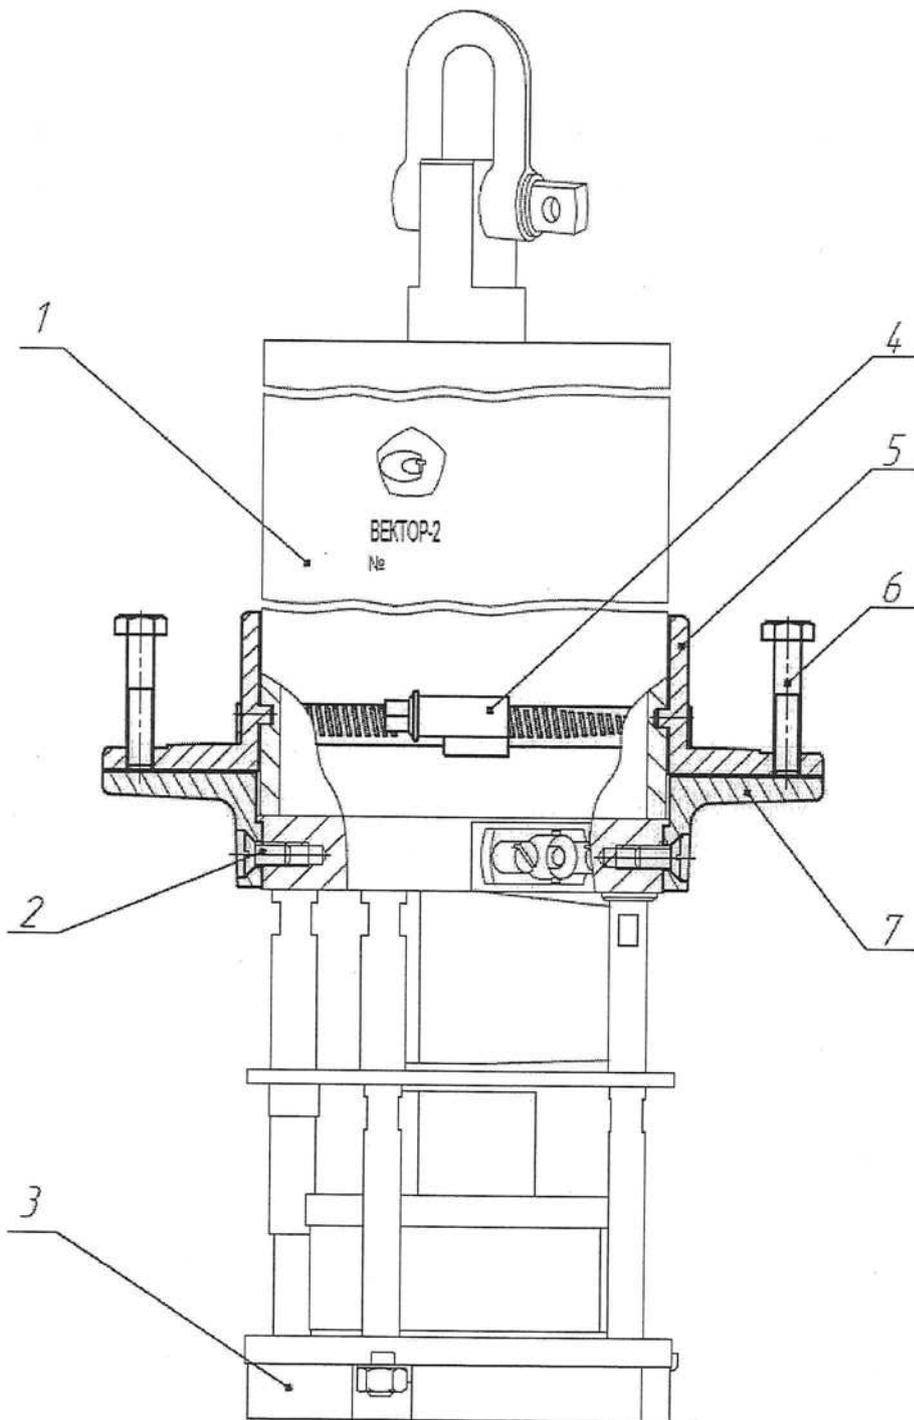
Установка съемника при расстыковке верхней и нижней частей корпуса измерителя
